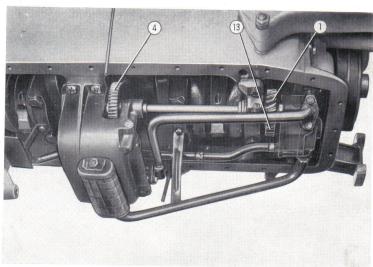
Equilibratore a masse centrifughe montato sul motore.
